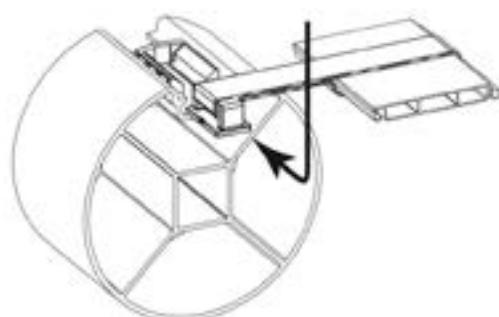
Giunzione tra il piazzale e l'asse delle lamelle
